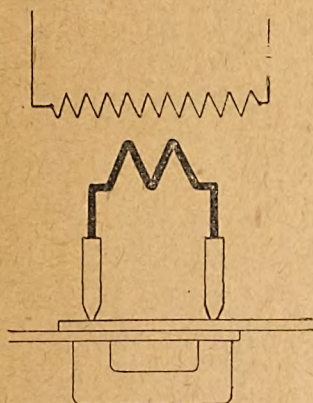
Soudure en 2 points avec 1 transformateur.
